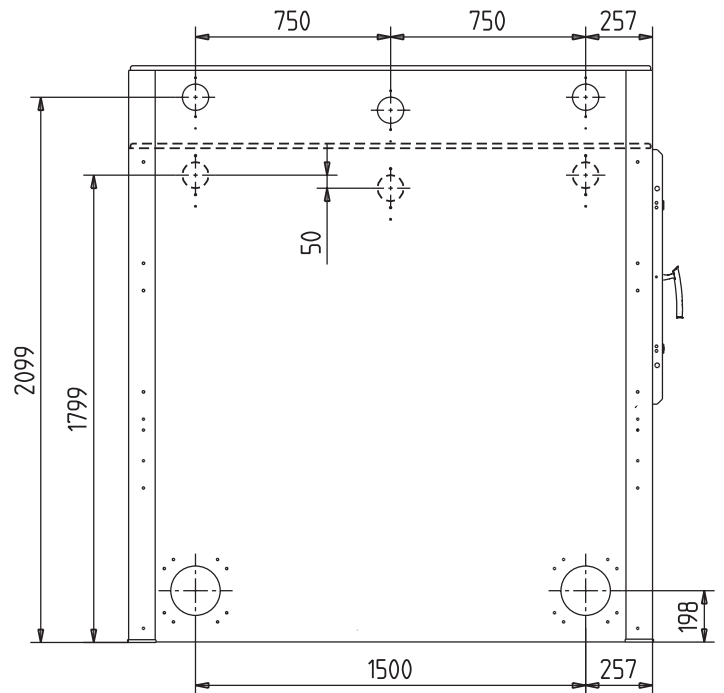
Stahlblech-Tanks mit Breite 2,0 m
